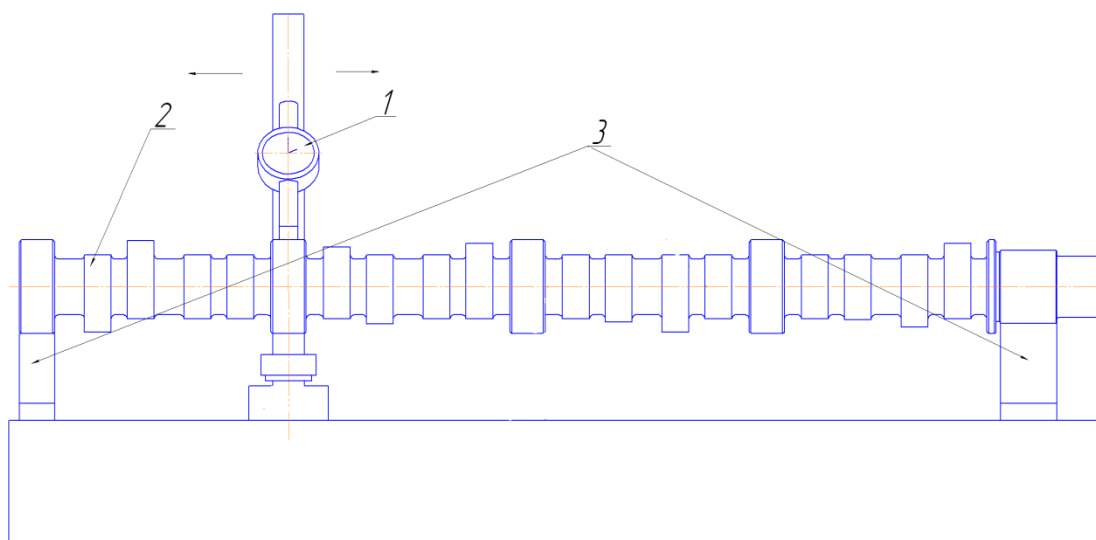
Контрольно-измерительный прибор: 1 – часовой индикатор; 2 – распределительный вал; 3 – призмы опорные.
